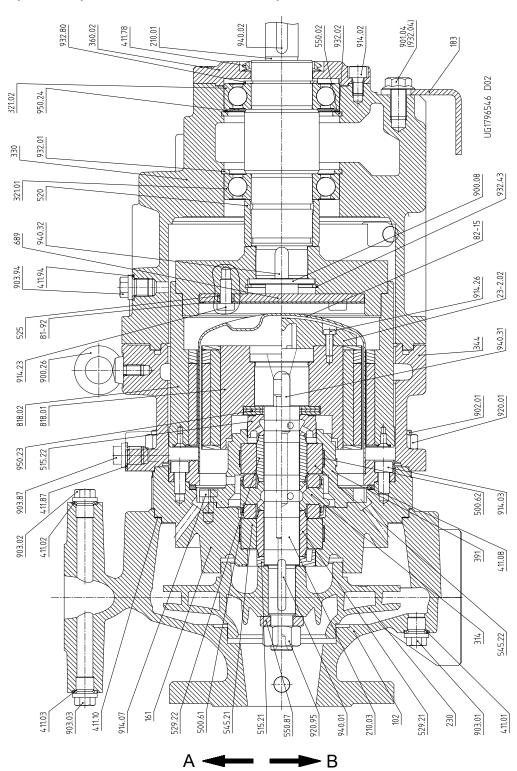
Сборочный чертеж, исполнение с зажимной крышкой без переходника
